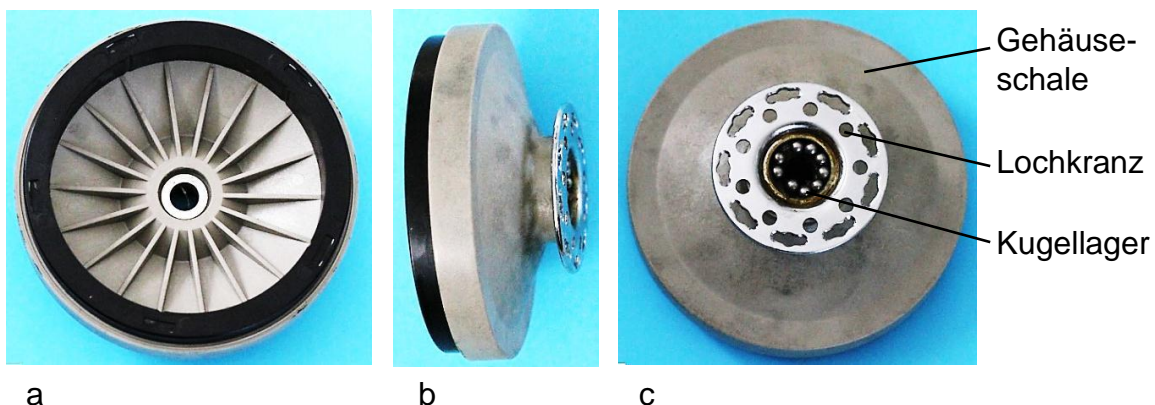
Gehäuseschale: a) Eingepresstes Magnetsystem: b) Seitenansicht, c) Gehäuseschale mit Lochkranz
